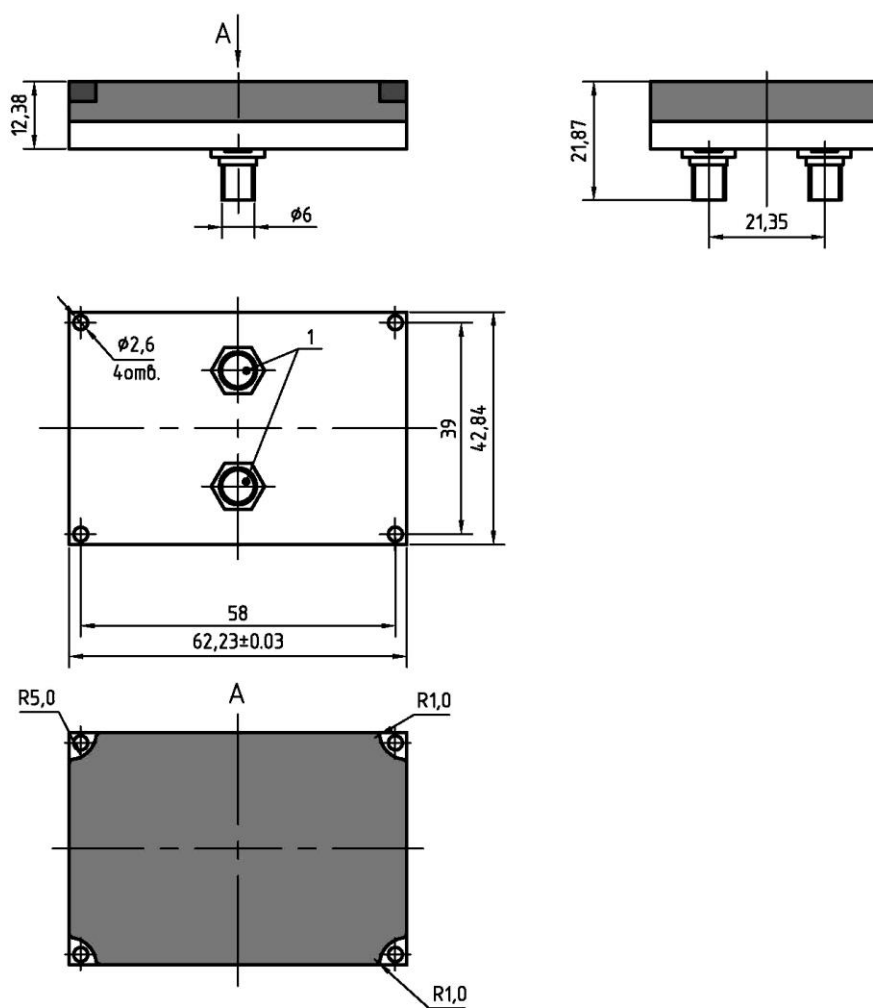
Габаритный чертеж адаптивной антенной решетки
